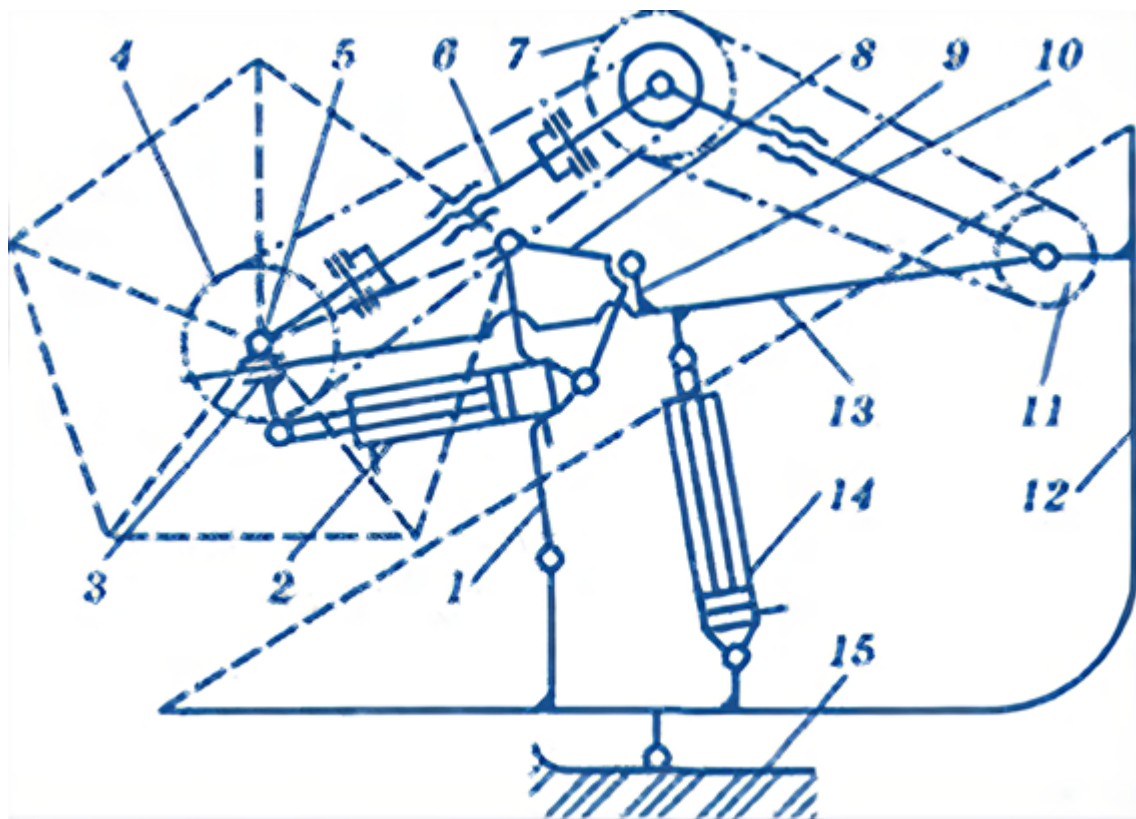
Схема заблокованого механізму регулювання положення мотовила:
